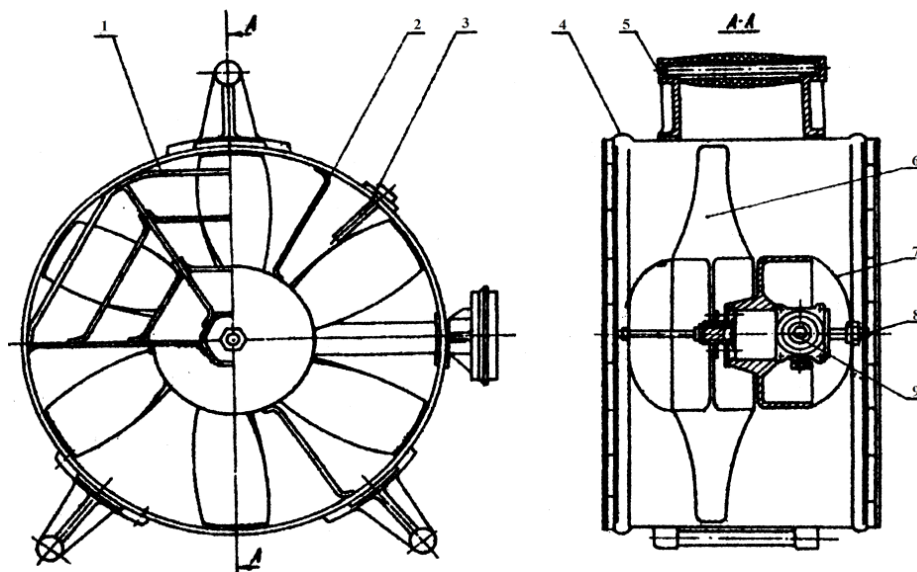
Димовсмоктувач ДП-7: 1 – захисна сітка; 2 – спиця; 3 – термометр; 4 – корпус; 5 – ручка; 6 – робоче колесо; 7 – обтікач; 8 – маслянка; 9 – редуктор
